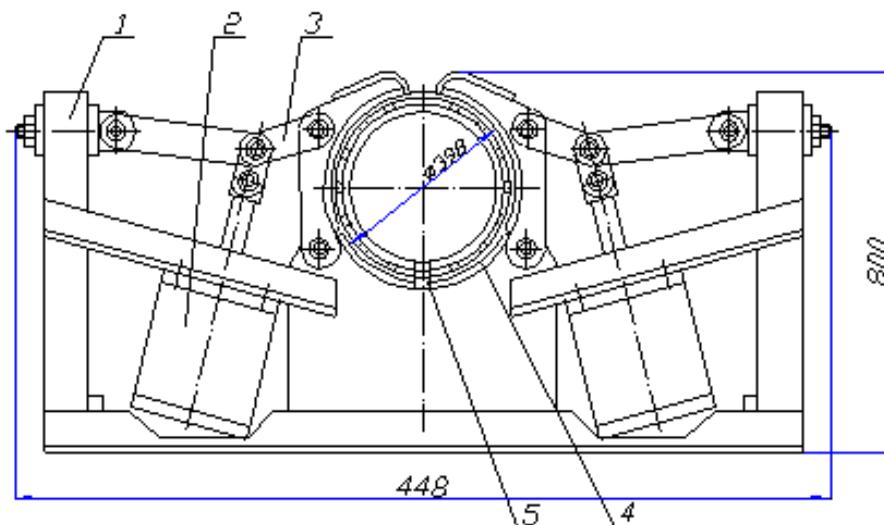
Схема станда для сборки продольных стыков обечаек небольшого диаметра
